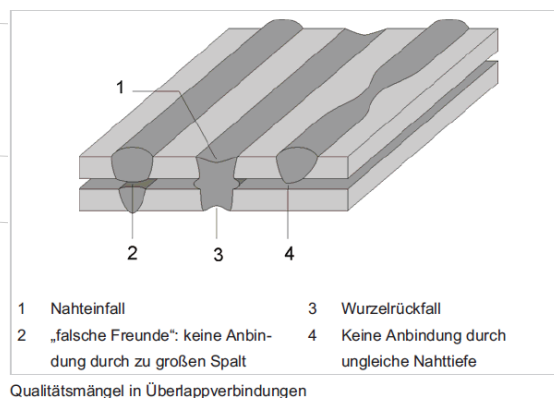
Qualitätsmängel von Schweißnähten]
